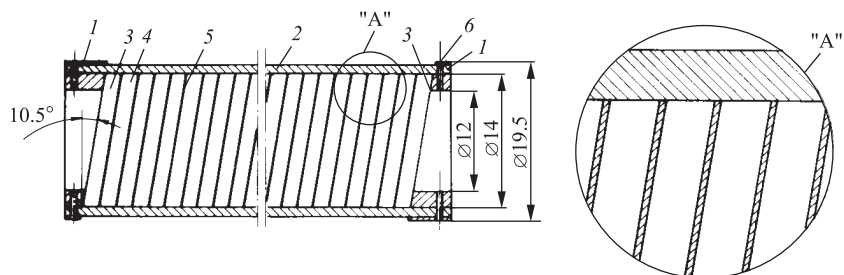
Конструкция ферромагнитного резонатора нейтронов: 1 — заслонки; 2 — корпус; 3 — пластинки из нержавеющей стали; 4 — алюминиевые прокладки; 5 — фольги пермаллоя; 6 — фиксирующие болты
